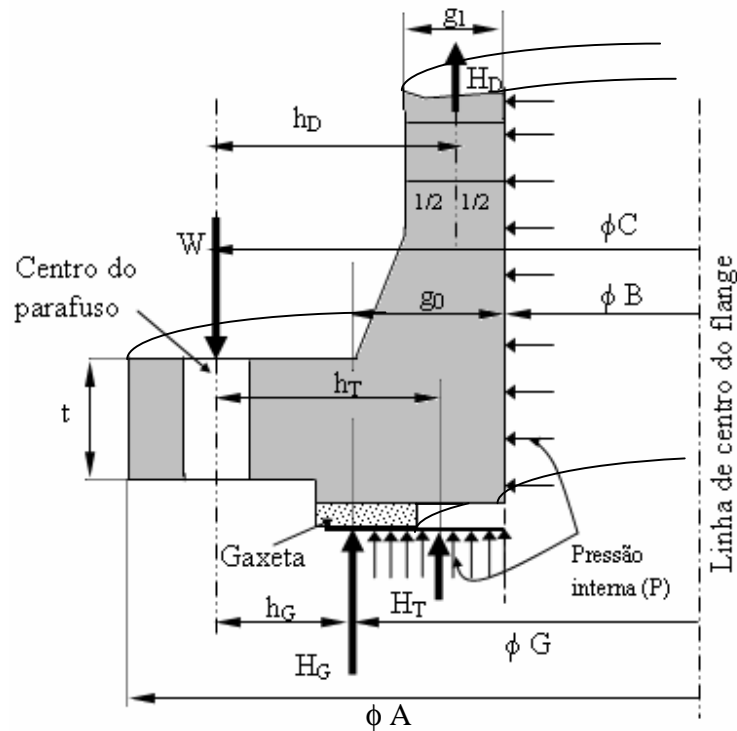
Principais dimensões, forças e reações envolvidas no projeto do flange
